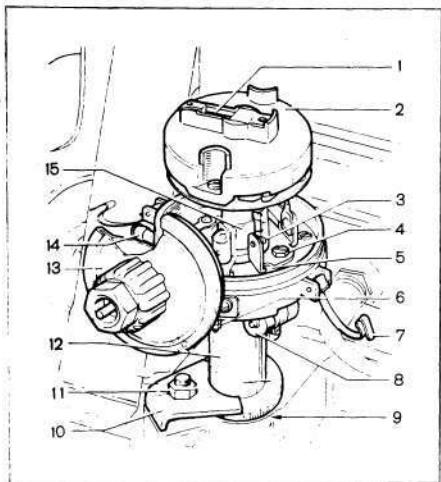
Распределитель зажигания: 1 — помехо-подавляющее сопротивление; 2 — бегунок; 3 — контакты прерывателя; 4 — винт; 5 — паз; 6 — клемма; 7 — пружинная защелка; 8 — конденсатор; 9 — шкала; 10 — кронштейн; 11 — гайка; 12 — корпус; 13 — вакуумный корректор; 14 — масленка; 15 — кулачок
